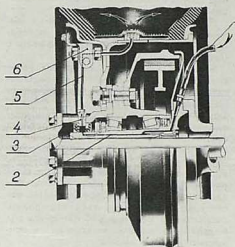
Головка подвода воздуха к шине: 1 — шланг; 2 — кольцевой канал; 3 — головка подвода воздуха; 4 — штуцер; 5 — трубка; 6 — запорный кран.
